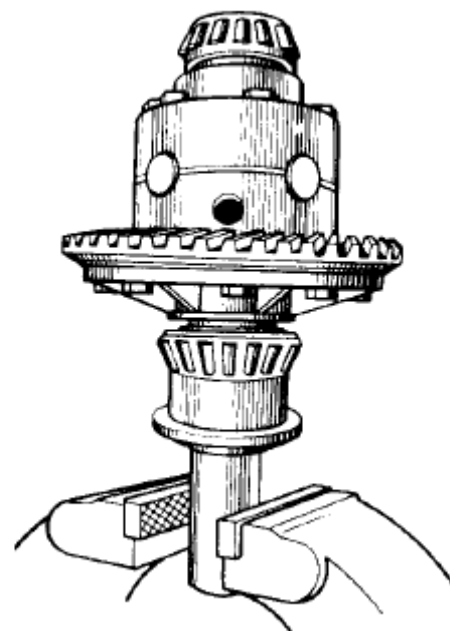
Предварительная напрессовка внутренних колец подшипника дифференциала
